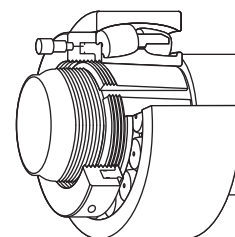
Tuerca hidráulica que se utiliza para montar el rodamiento sobre un manguito adaptador de empuje.
